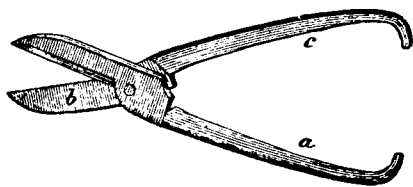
Ножницы для разрѣзанія металлическихъ листовъ.
